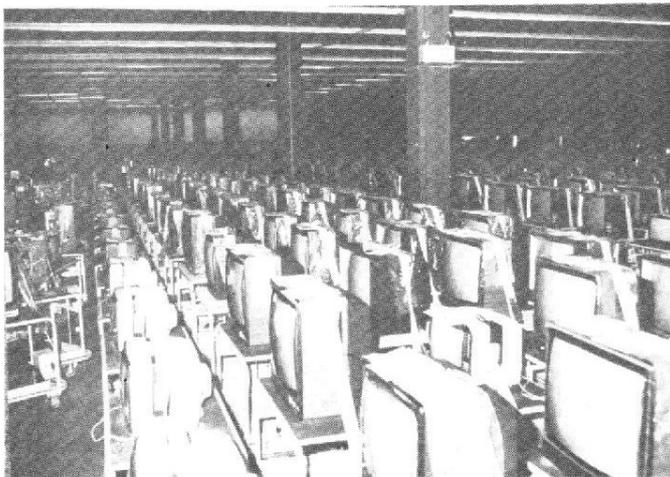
La salle de torture des téléviseurs. Ils subissent ici un test de 24 heures avant de passer aux réglages.
